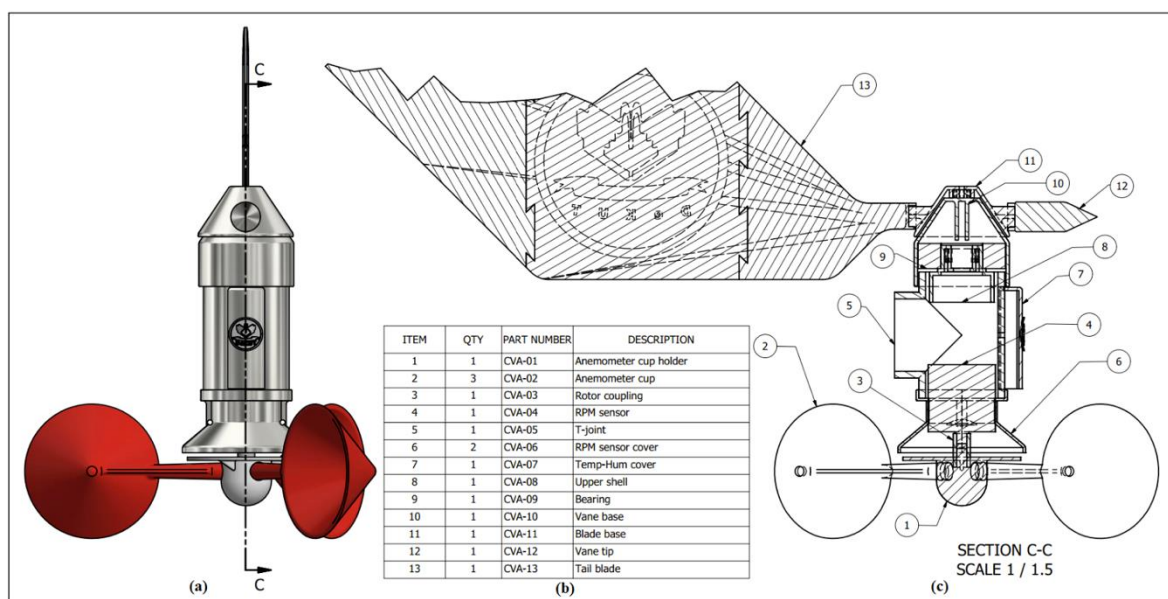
Ensamblaje virtual de la copa-aleta: (a) ensamblaje completo; (b) lista de piezas y (c) vista en sección (C-C). [13]
